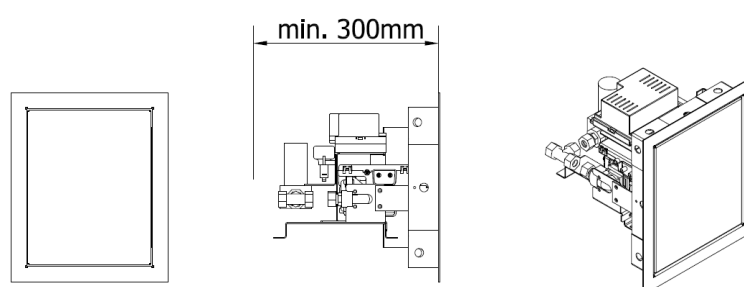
Taille minimale pour les besoins de l'installation d'un assemblage de gaz
